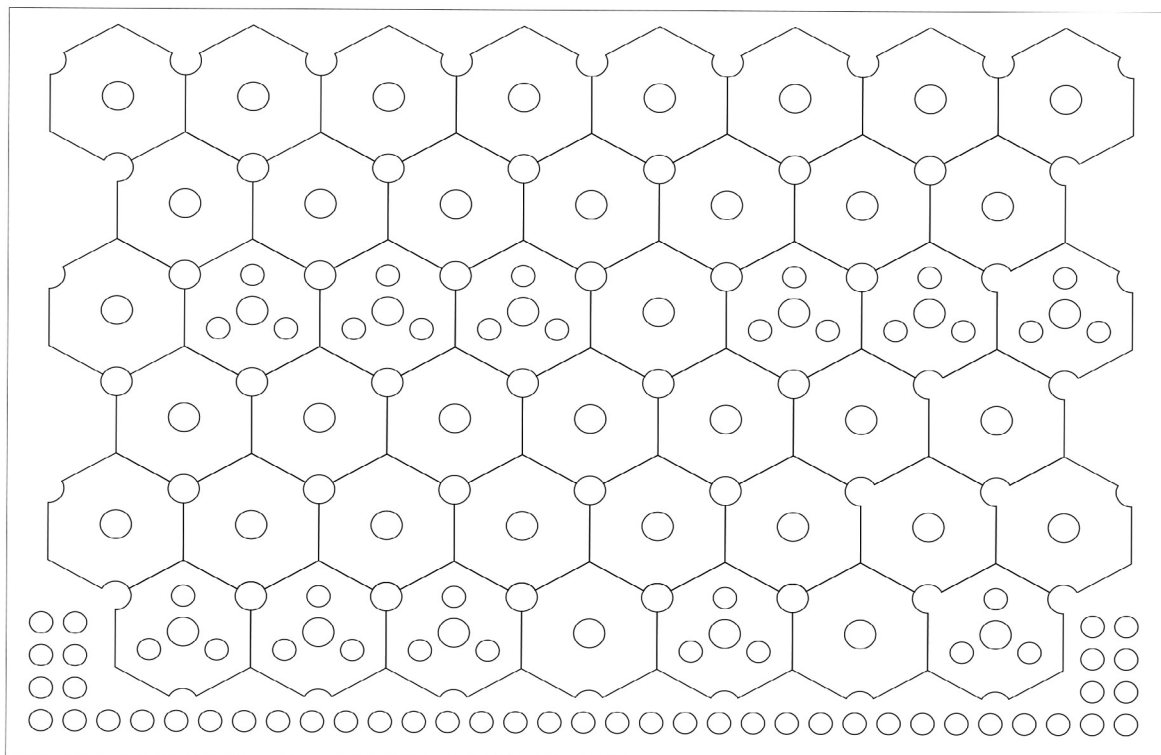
Dibujo en planta para aprovechamiento de tablero.
